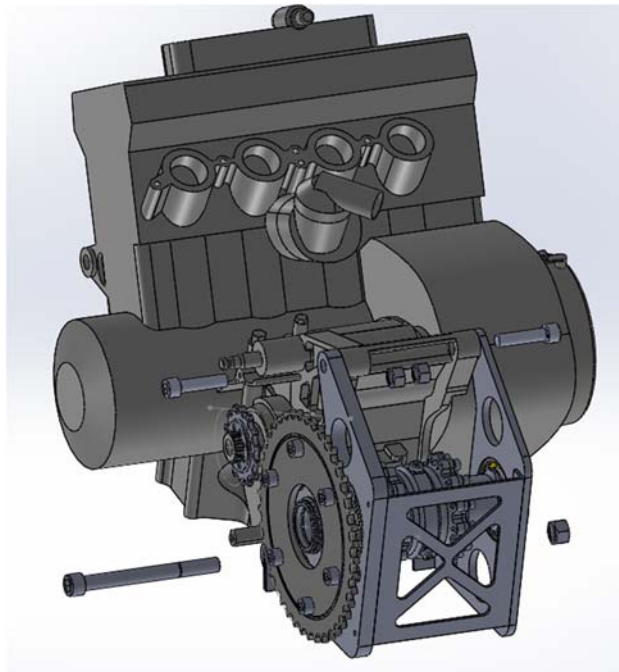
Montaje final de la transmisión, unión del conjunto porta diferencial al motor.
